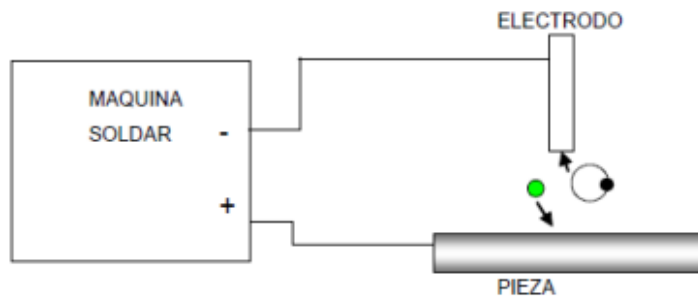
Esquema de Polaridad Directa de la Soldadora GMAW.
